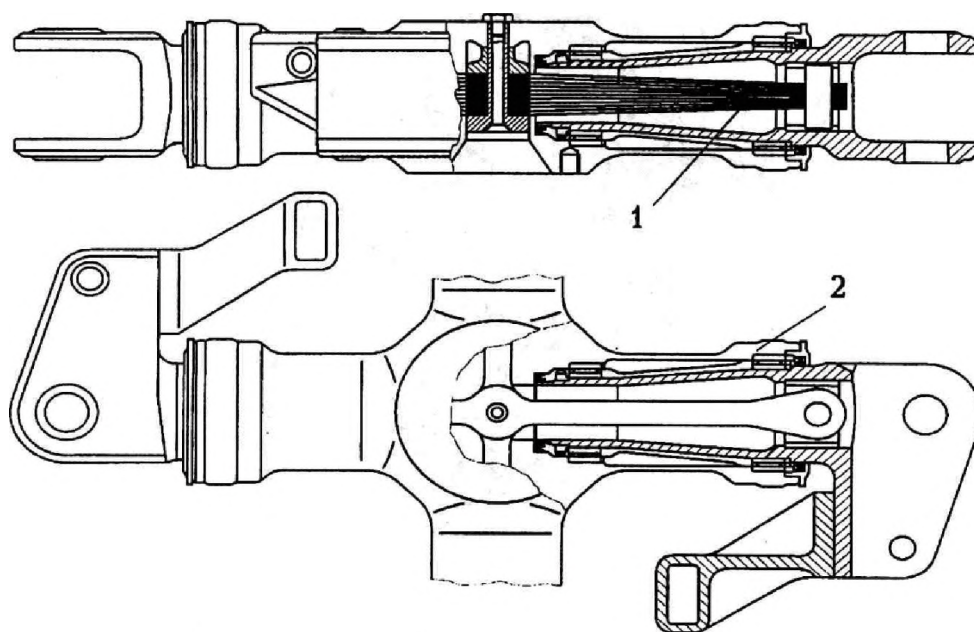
Жесткая втулка НВ вертолета Во105 с торсионом ОШ [7]: 1- пластинчатый торсион, 2- корпус осевого шарнира. 3 – корпус втулки; 4 – рычаг поворота лопасти.
